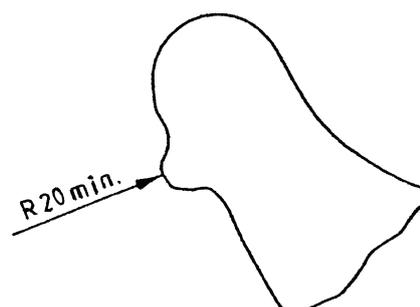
Formenprofile mit geeigneten, gerundeten Ecken
